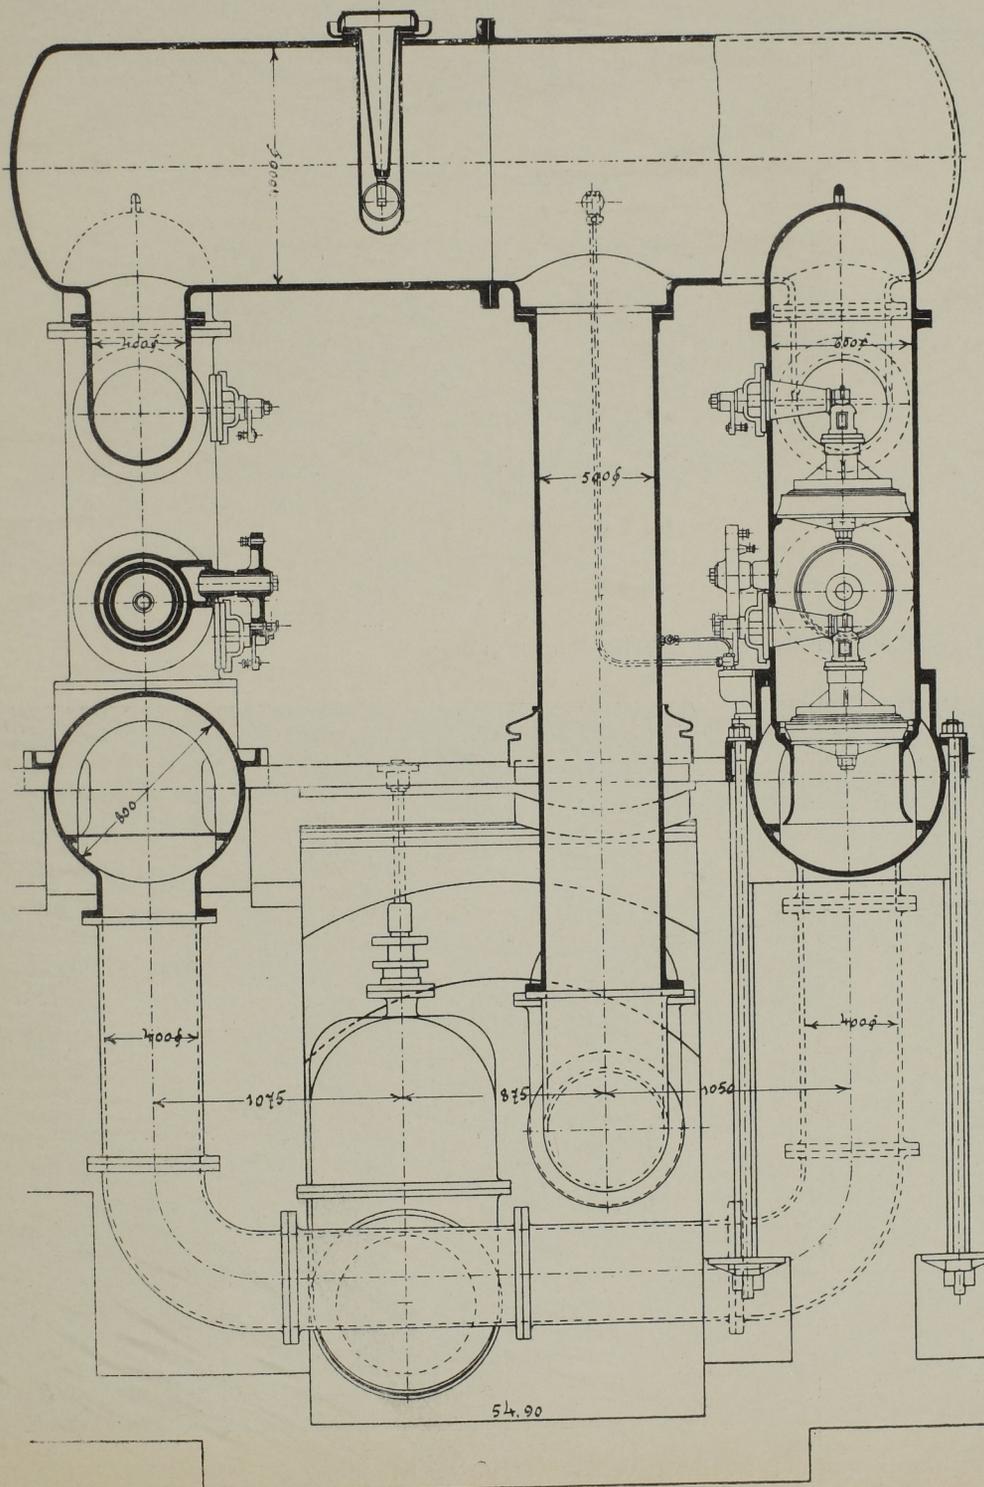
Querschnitt durch die Pumpe. Massst. 1:30.
